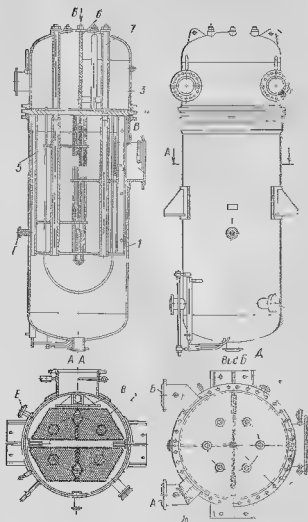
Подогреватель низкого давления типа ПН. 1 — корпус подогревателя 2 — трубный пучок 3 — водяная камера 4 — трубная доска 5 — вертикальные перегородки 6 — щиток отбойный 7 — выход конденсата 8 — отбойный щиток А — вход основного конденсата Б — выход основного конденсата В — вход пара Г — отток воздуха Д — выход конденсата Е — подвод воздуха Ж — подвод конденсата
